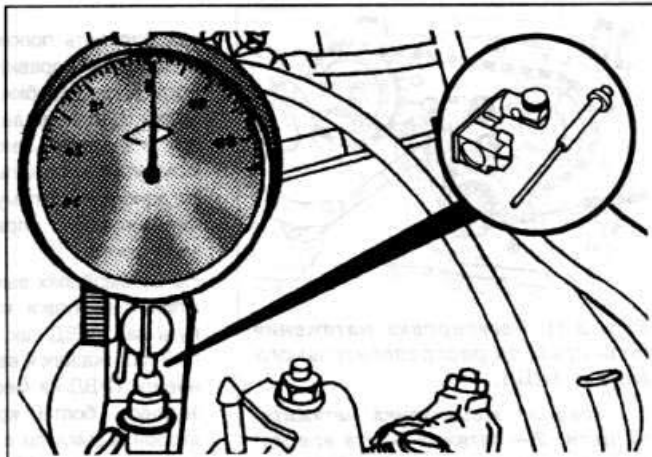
Установка ножки индикатора на внутреннюю ступеньку переходника на автомобилях выпуска с 1988 г.
